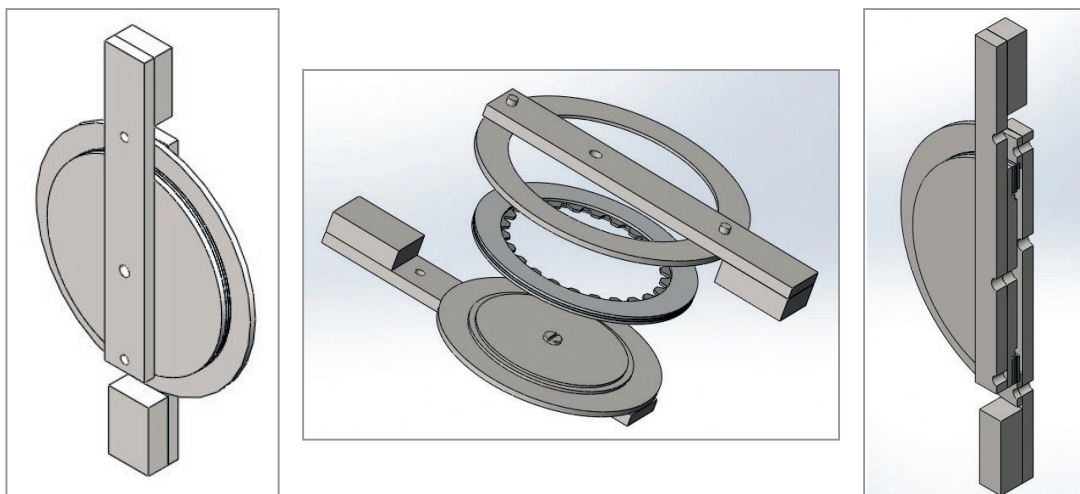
Принципиальная схема приспособления для испытаний на сдвиг ведомого диска сцепления
